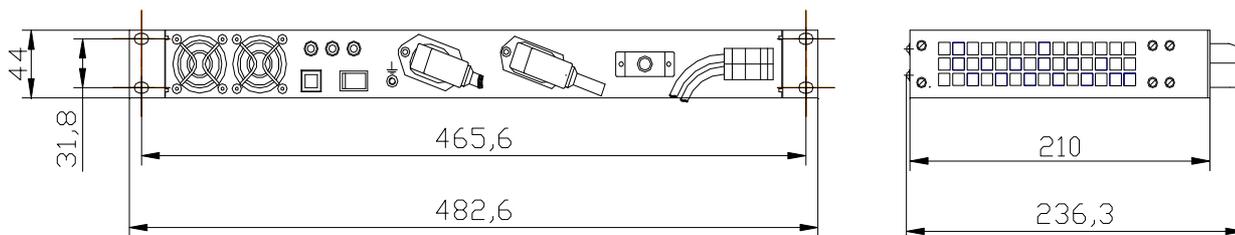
Габаритный чертеж ИЦ-600БП-19
